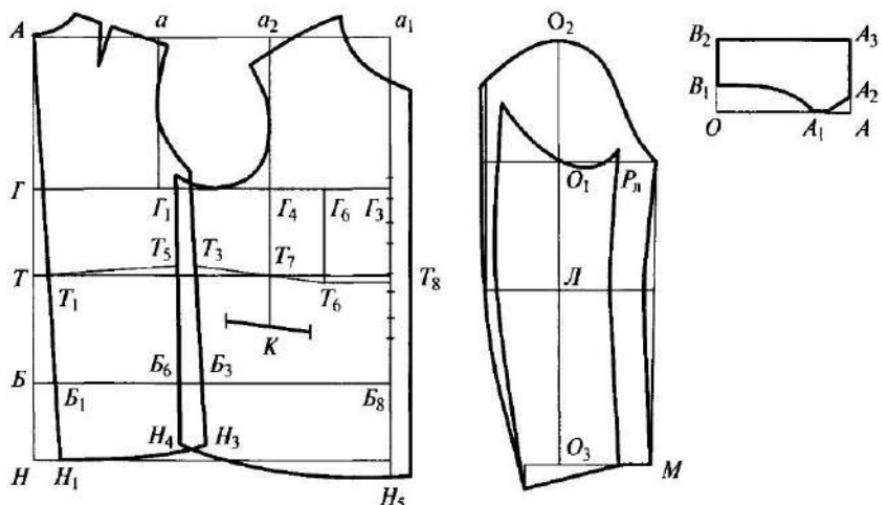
Возможная схема чертежа основы мужской куртки из нетканого материала
